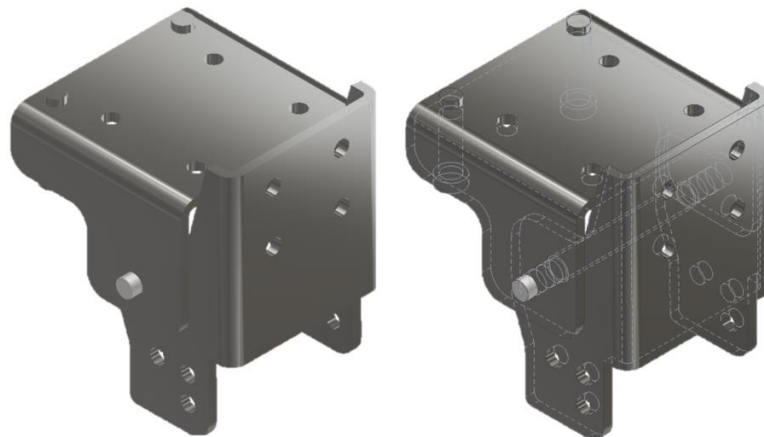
Pojednostavljeni geometrijski model sklopa šarke – engl. exploded view
